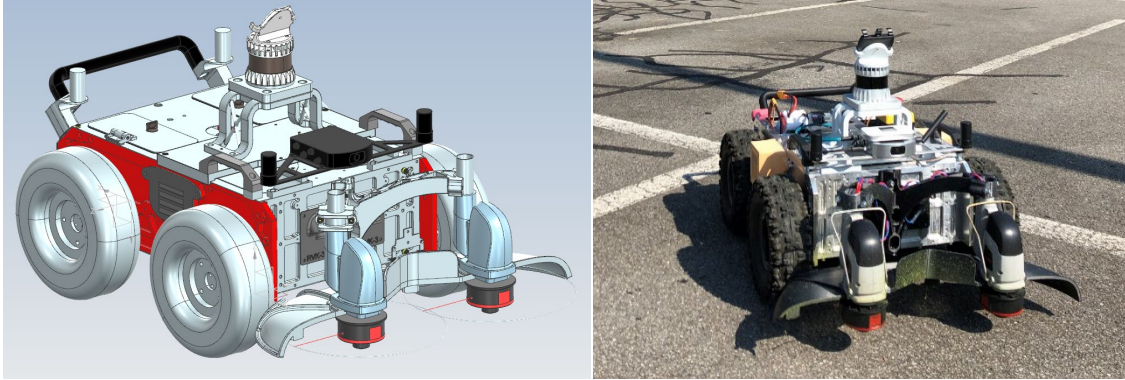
CAD Design und Realisierung des S-bot Prototyps
